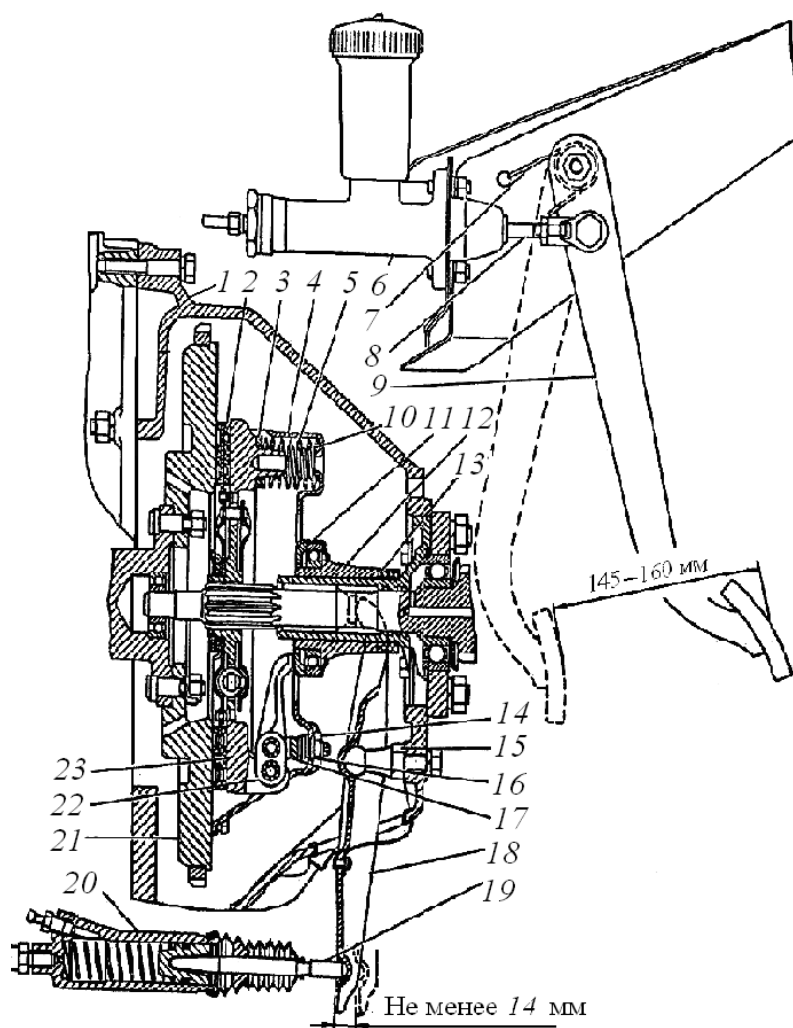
Пружинно-рычажное сцепление и привод выключения сцепления: 1 – картер сцепления; 2 – ведомый диск сцепления; 3 – теплоизолирующая шайба; 4 – кожух; 5, 10 – пружина нажимная; 6 – главный цилиндр выключения сцепления; 7 – оттяжная пружина педали; 8 – толкатель рабочего цилиндра; 9 – педаль; 11 – подшипник выключения сцепления; 12 – муфта выключения сцепления; 13 – поролоновые кольца; 14 – сферическая гайка; 15 – шаровая опора; 16 – коническая пружина; 17 – опорная вилка; 18 – вилка выключения сцепления; 19 – толкатель рабочего цилиндра; 20 – рабочий цилиндр привода выключения сцепления; 21 – маховик; 22 – рычаг выключения сцепления; 23 – нажимной диск
